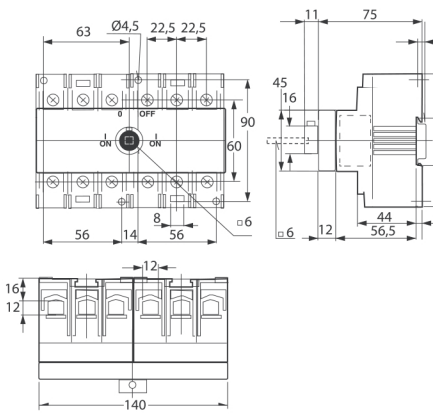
Габаритные и установочные размеры реверсивных рубильников 100А
